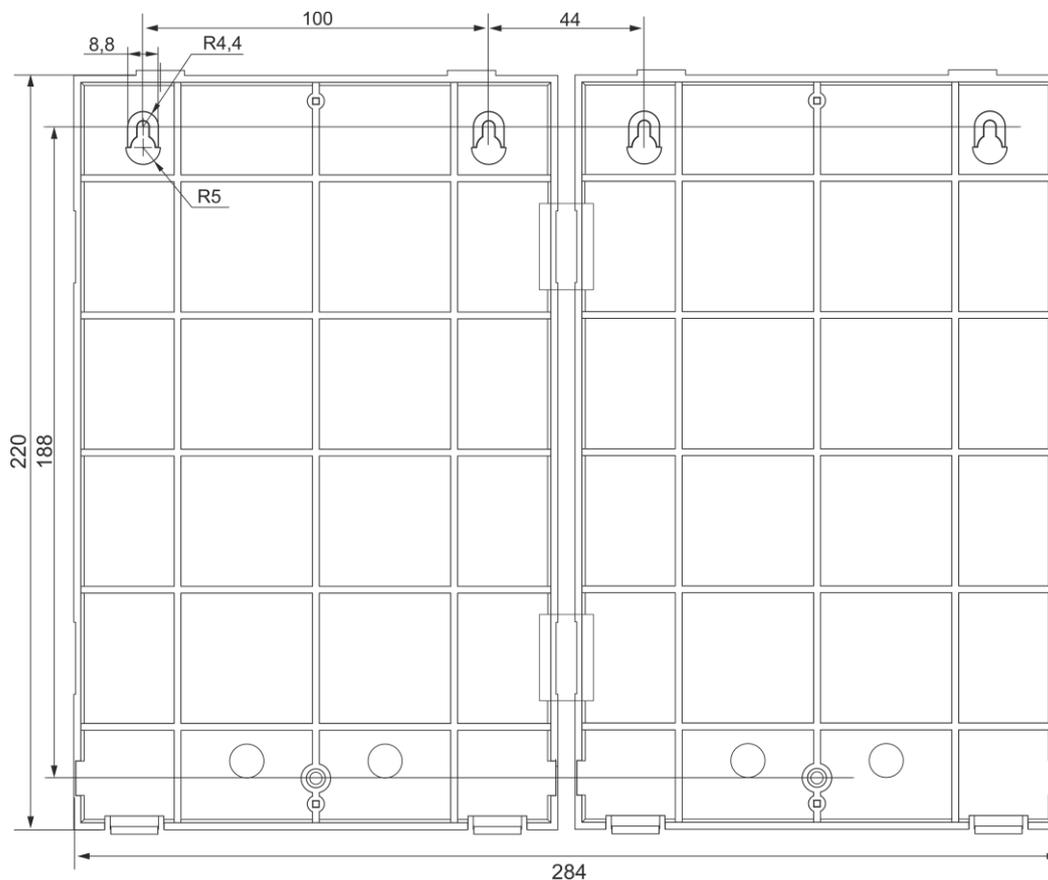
Установочный чертеж основания корпуса ППКПиУ серии «А24» и бокса аккумуляторного БА-18
